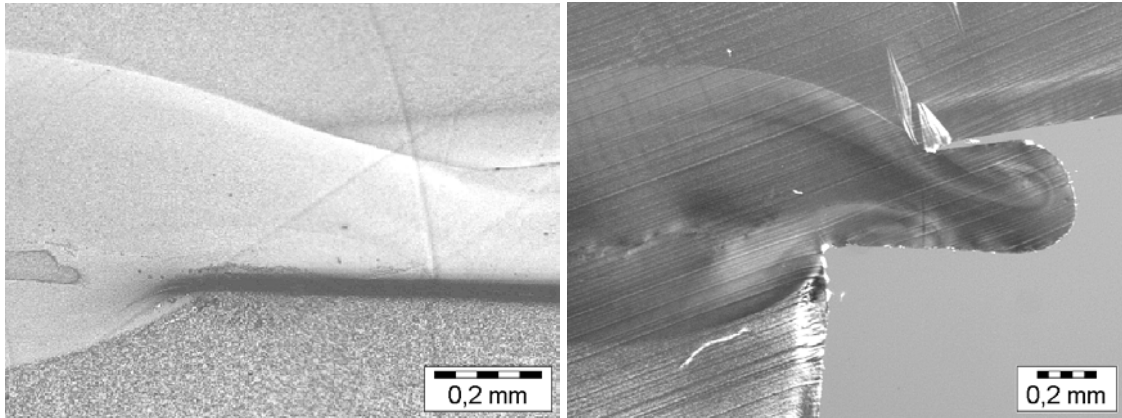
Schweißnahtserie S7; stereomikroskopische Aufnahmen
